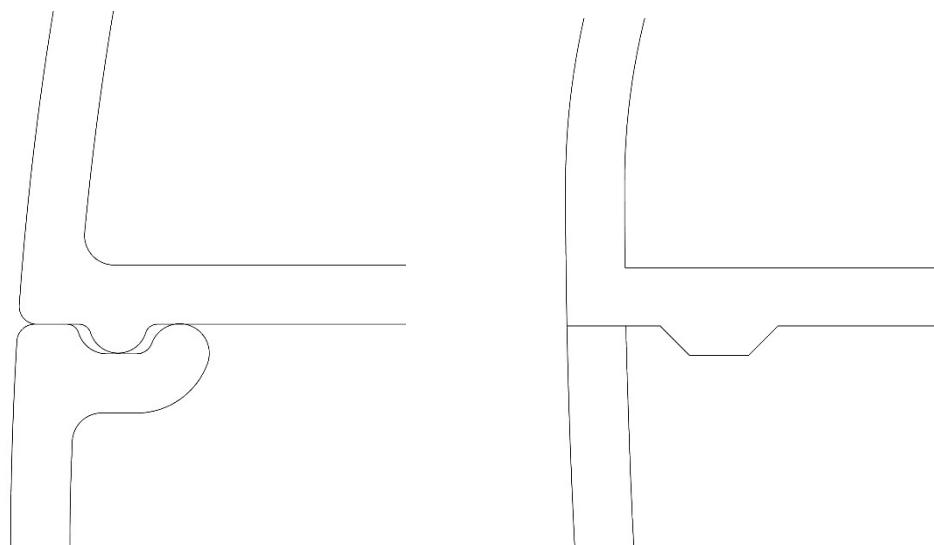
Desenho técnico dos encaixes dos filtros 1 (esquerda) e 2 (direita)
